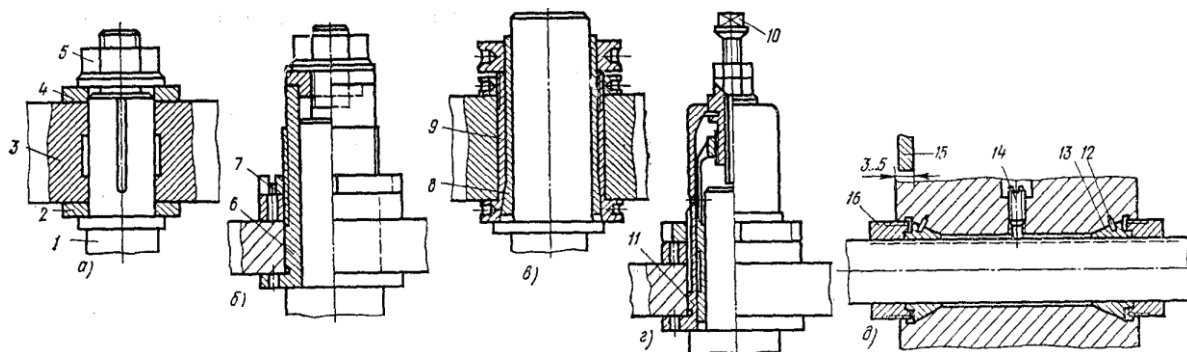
Способи кріплення різальних інструмент у чотирибічних поздовжньо-фрезерних верстатах: а — з посадкою на шпиндель, б — за допомогою перехідної втулки, в — на цанговому оправленні, г — на настановній головці, д — на двох коротких конусних цангах; 1 — шпиндель, 2 — проставочне кільце, 3 — фреза, 4 — шайба, 5, 16 — затяжні гайки, 6, 9 — втулки, 7 — гайка, 8 — конусна розрізна втулка, 10 — гвинт; 11 — настановна головка, 12 — штифт, 13 — коротка цанга, 14 — напрячний гвинт, 15 — напрямна лінійка
